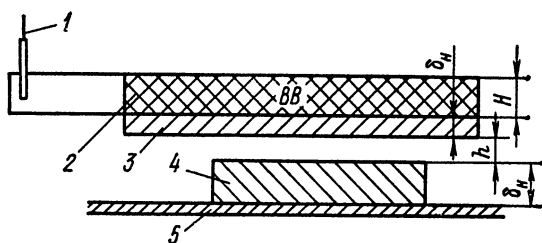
Схема сварки взрывом двух пластин
